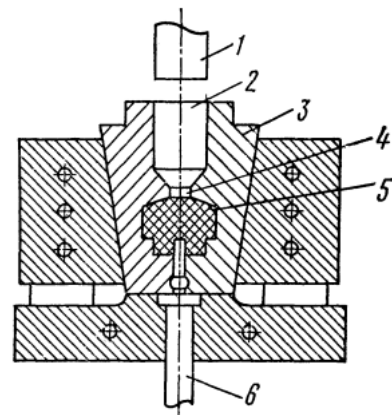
Схема прес-форми для литтєвого пресування: 1 – нагнітальний шток; 2 – завантажувальна камера; 3 – рознімна матриця; 4 – ливниковий канал; 5 – заповнена матеріалом оформлювальна порожнина; 6 – виштовхувач
